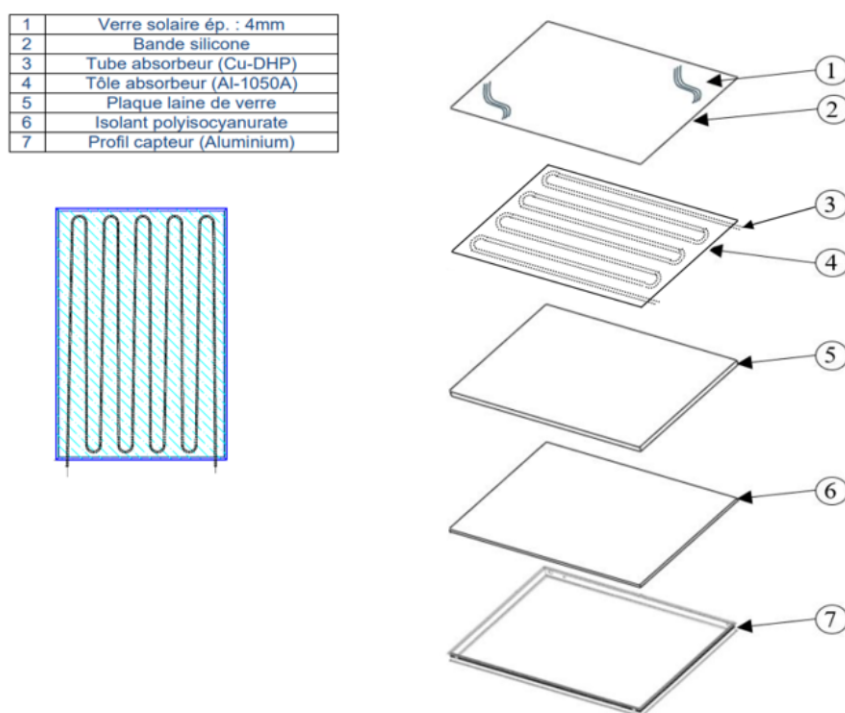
Vue d'ensemble du capteur CSH avec nomenclature et matière
